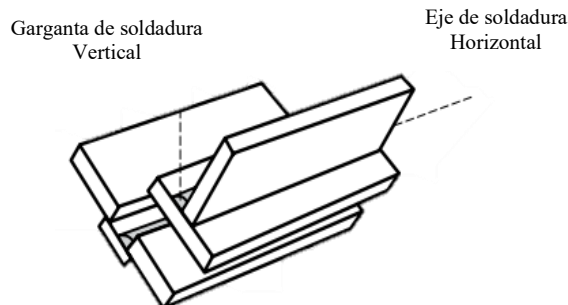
Posición de prueba para soldadura de planchas 1F
